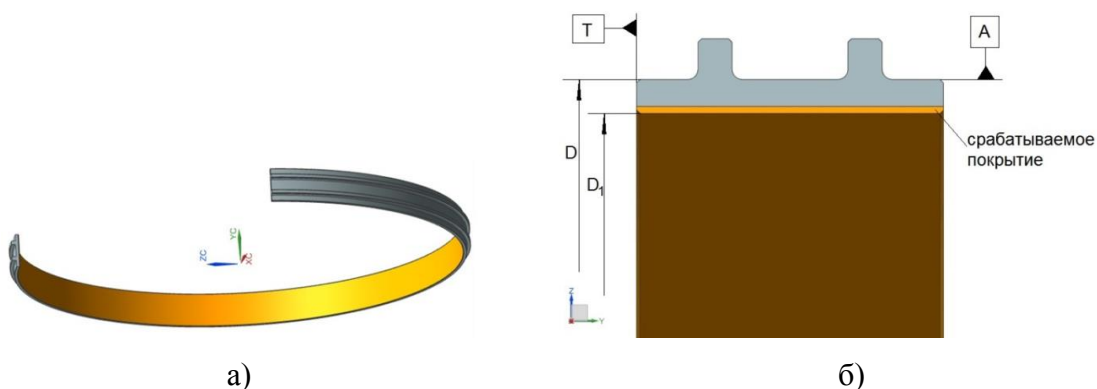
Кольцо корпуса компрессора ГТД:
